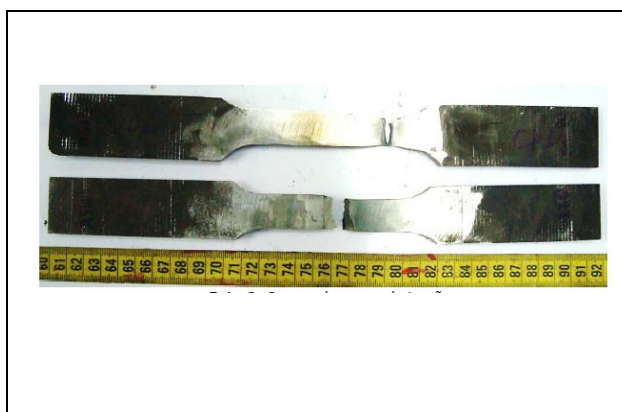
CORPOS DE PROVA SOLDADOS APÓS ENSAIO DE TRAÇÃO
